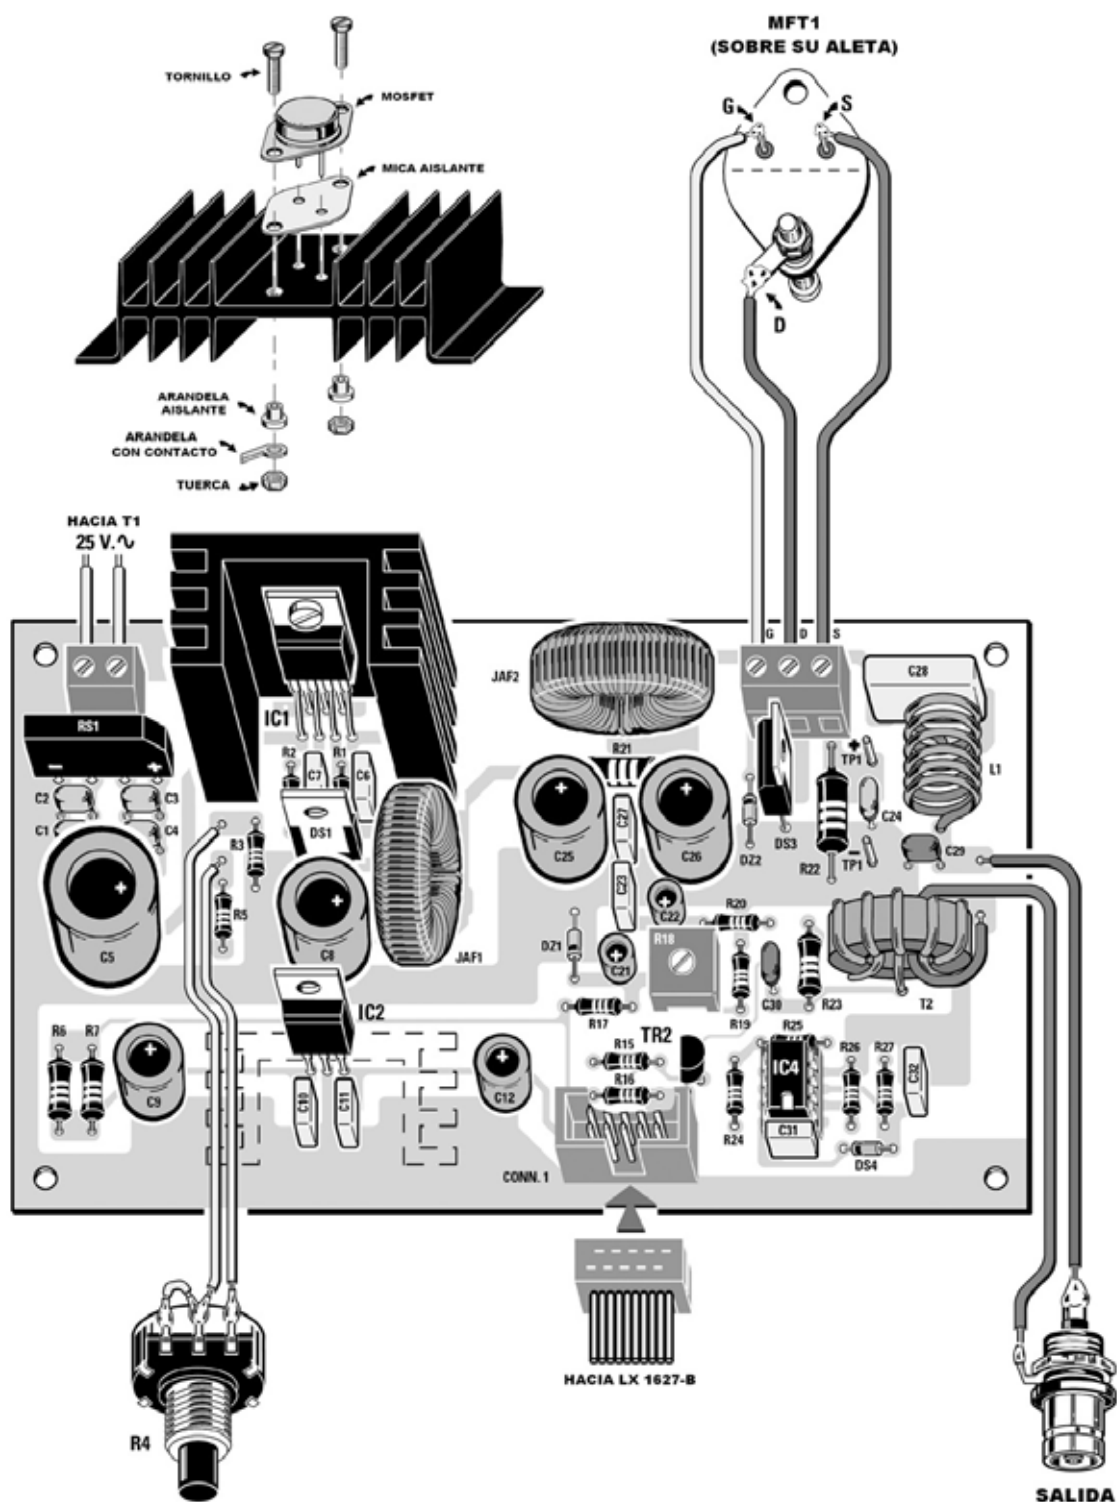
Esquema práctico de montaje del Generador de Ultrasonidos. Para realizar el montaje del MOSFET IRF321 sobre su aleta de refrigeración hay que utilizar la mica y las arandelas aislantes, tal y como se muestra en la parte superior-izquierda.
